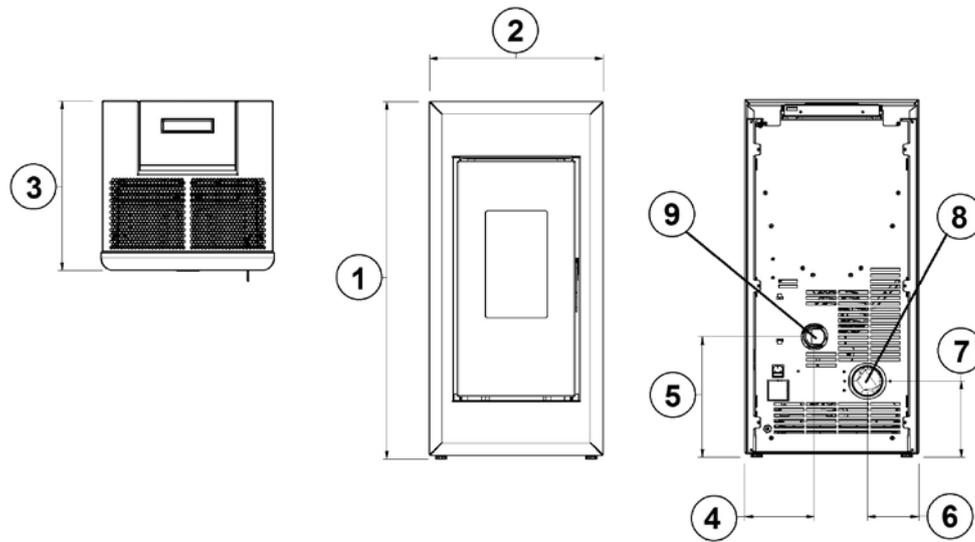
Γενικές διαστάσεις: ONE/BEAM AIRTIGHT
